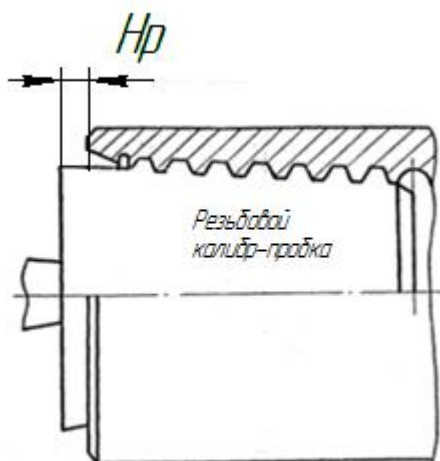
Схема контроля муфт диаметром 215,9; 244,5 и 269,9 мм резьбовым калибром-пробкой
